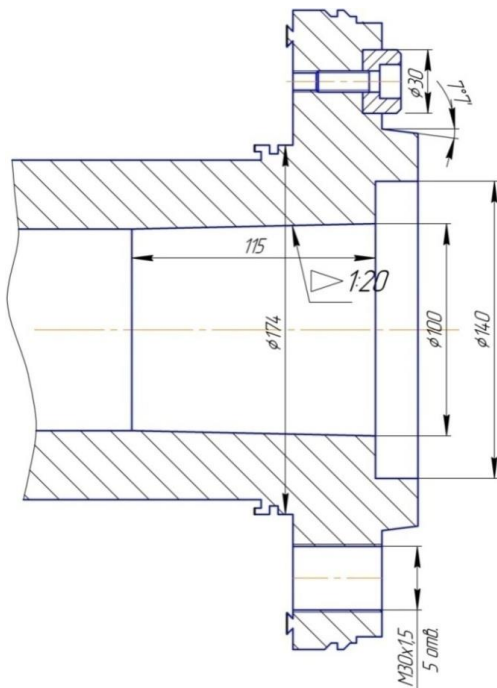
Конструкція переднього кінця шпинделя та його приєднувальні розміри
